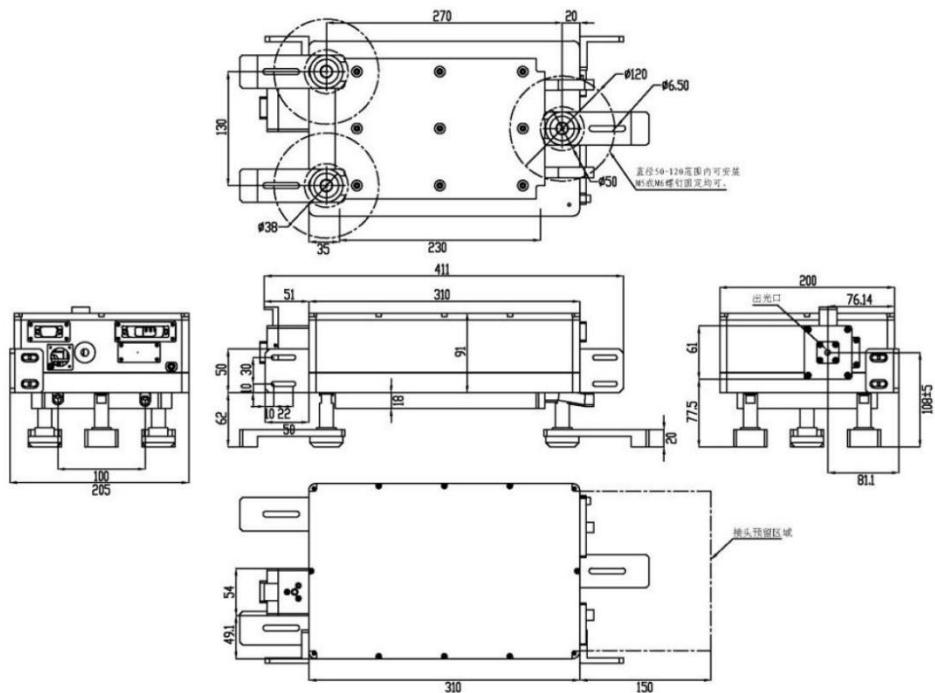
专家 II 系列水冷激光头安装尺寸 Fig.9.1 Expert II Series Water Cooled Laser Head Mounting Dimensions
